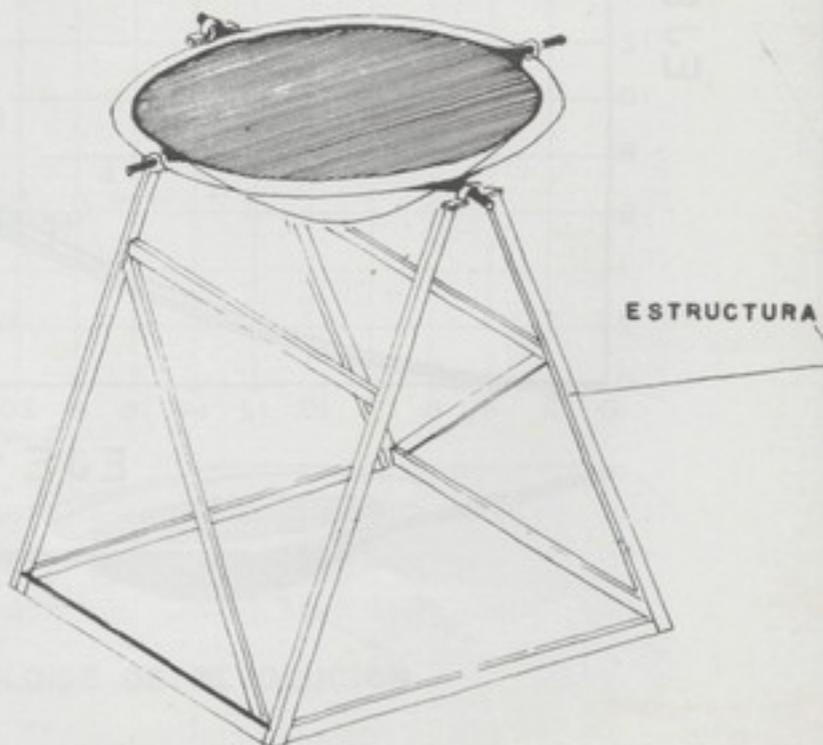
Lente plano convergente SOLIDO EN ESTRUCTURA DE SOPORTE
